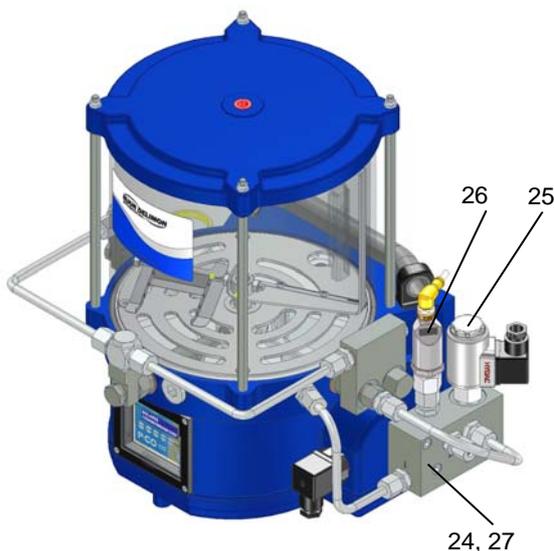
(Ausführung für Einleitungsanlage mit elektr. Umsteuerung)
